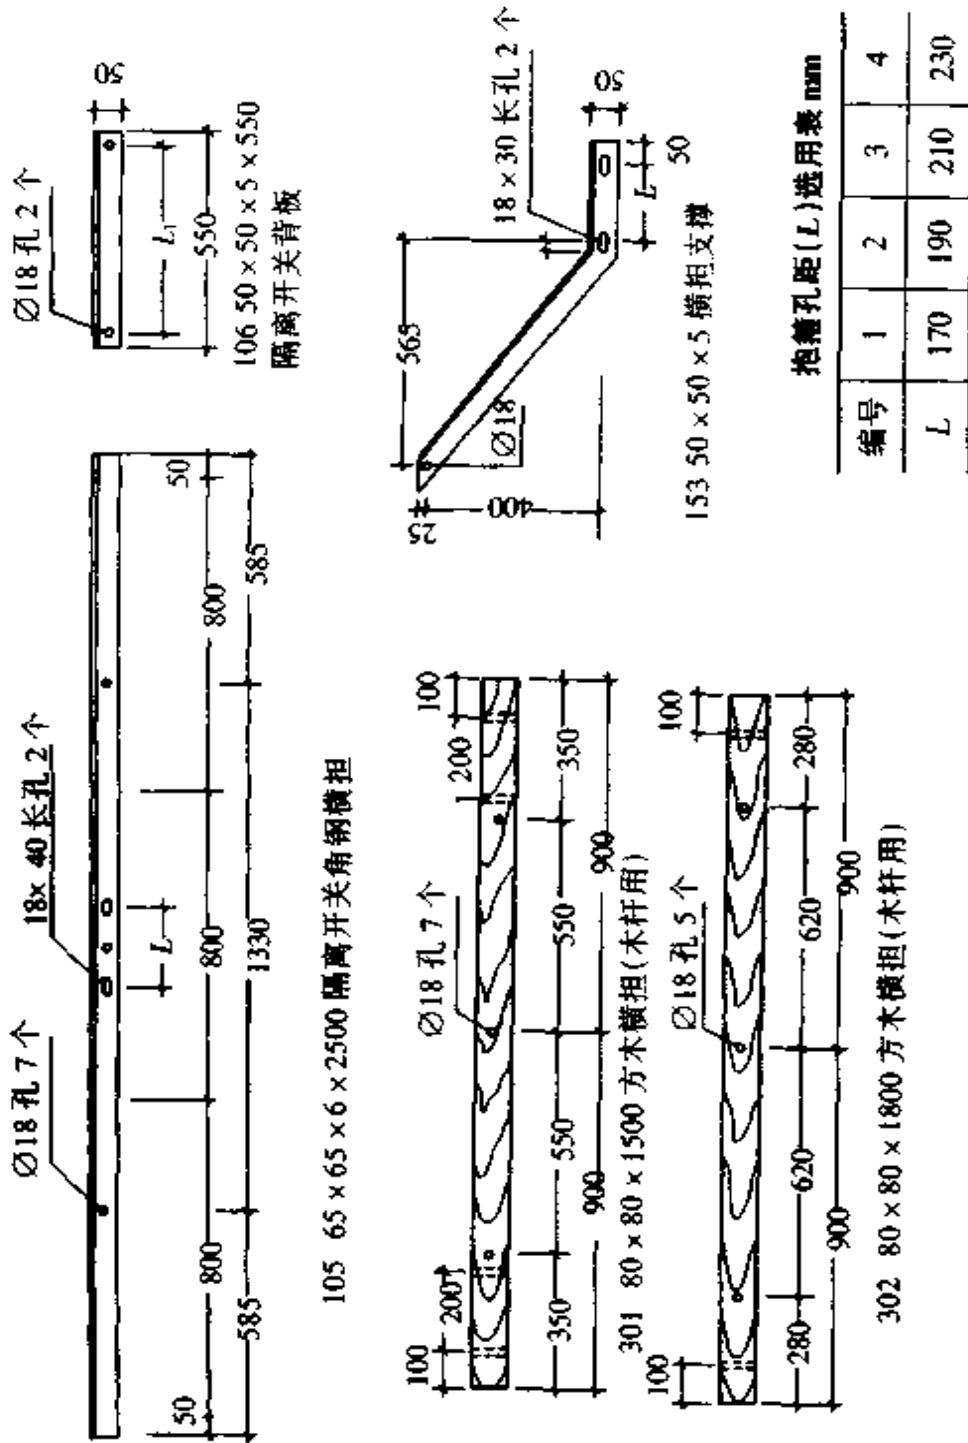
钢筋混凝土电杆附件加工图(三)
